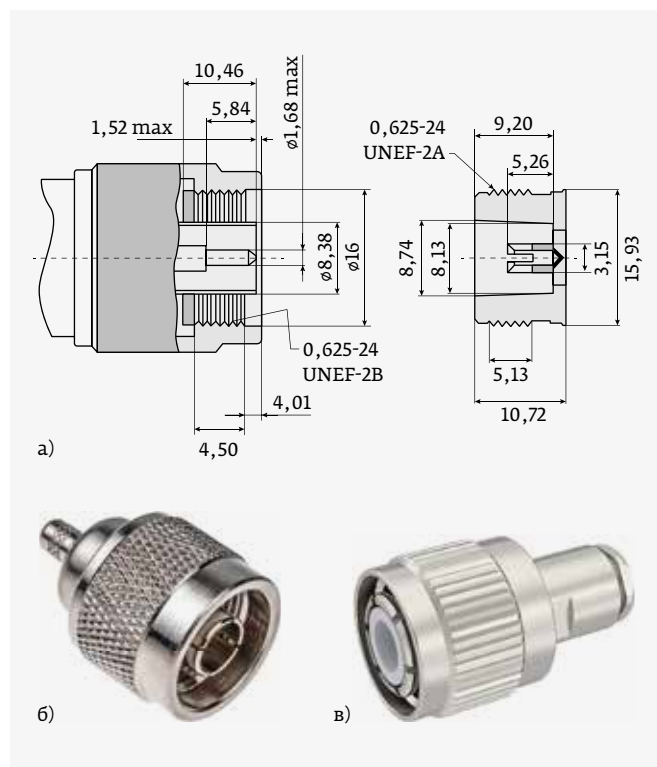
Соединители типа N. Интерфейс розетки и вилки (а), внешний вид соединителей N (б) и HN (в)
